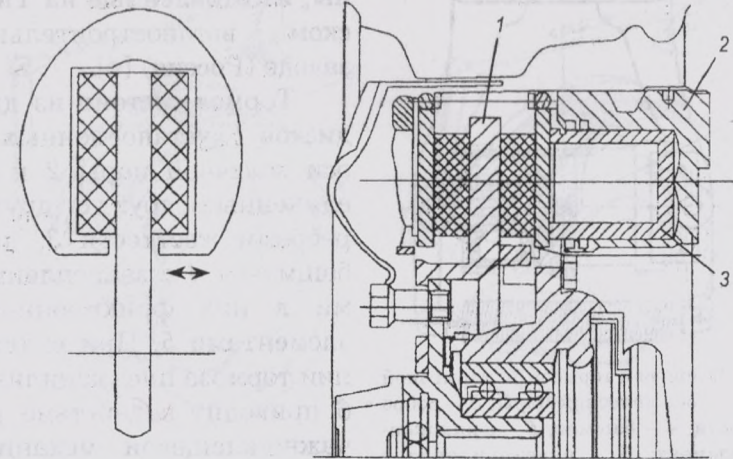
Дисково-колодочный тормоз автомобиля ВАЗ-2121 с плавающей скобой: 1 – тормозной диск; 2 – скоба; 3 – поршень
